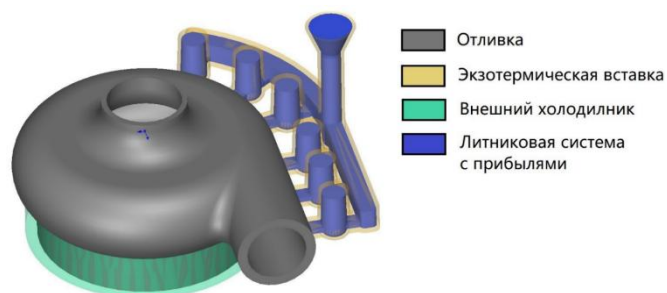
Трехмерная модель отливки улитка вместе с новой литниковой системой.
